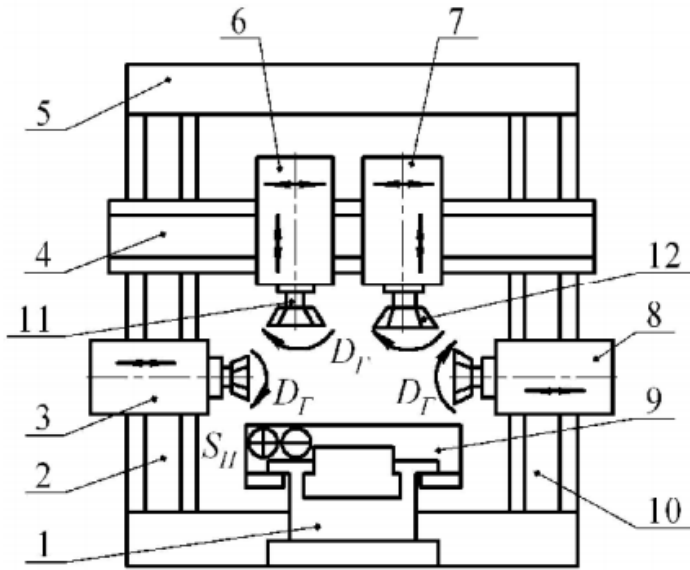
Двостойковий поздовжньо-фрезерний верстат
